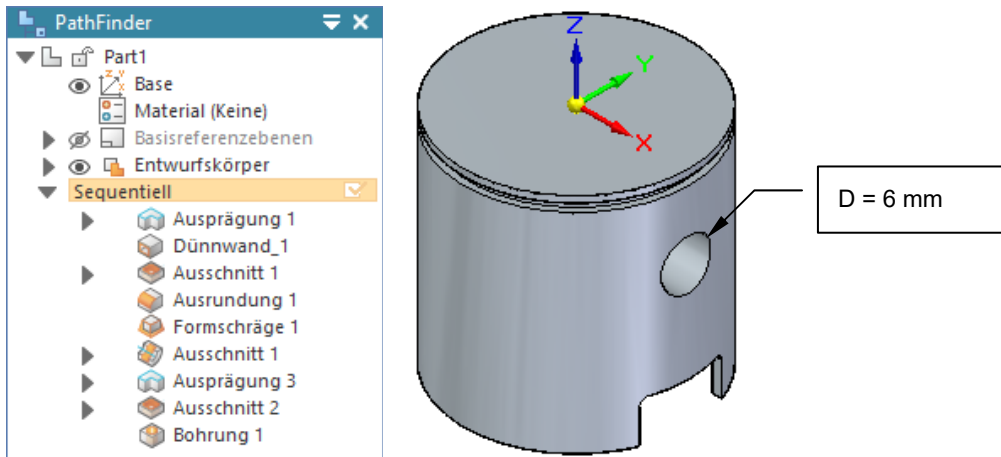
Die Bohrung für den Kolbenbolzen
